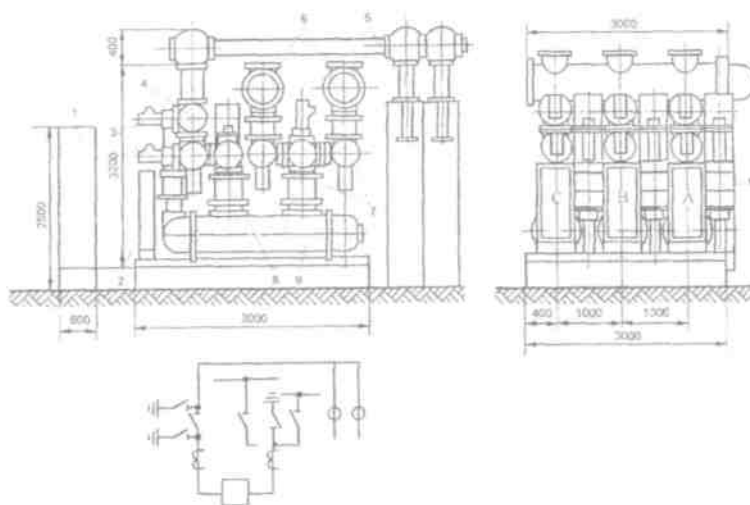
КРУЭ-110кВ. Ячейка линейная ЯЭ-110Л-23У4: 1 —распределительный шкаф; 2 — полюсный шкаф управления; 3 — заземлители; 4,7 — разъединители; 5 — кабельный ввод; 6 — системы трехфазных сборных шин; 8 — трансформаторы тока; 9 — выключатель; 10 — привод выключателя
